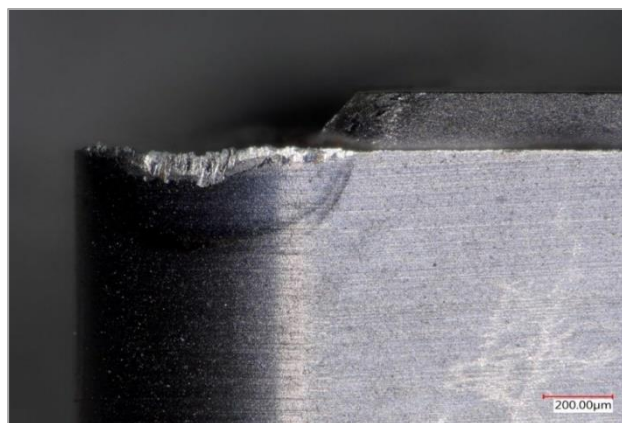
Usure abrasive de l'outil en carbure [9].
